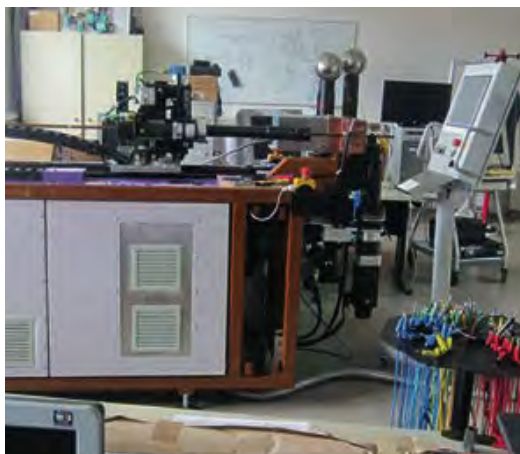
Der Prototyp des Bearbeitungsautomaten mit Heizsystem in unserem F&E-Labor.
